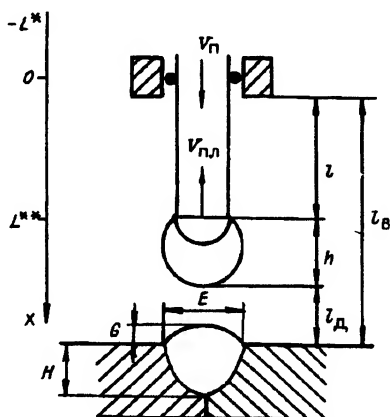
Схема роста капли расплавленного металла электрода и форма получаемого сварного шва.
